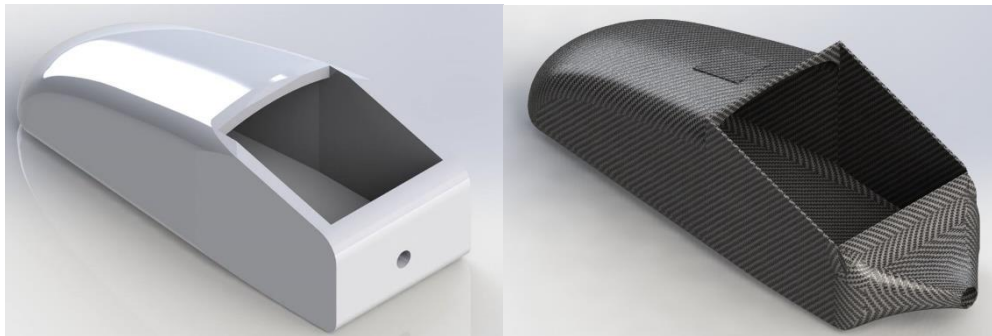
Diseño preliminar (izq.) vs diseño final (der.)
